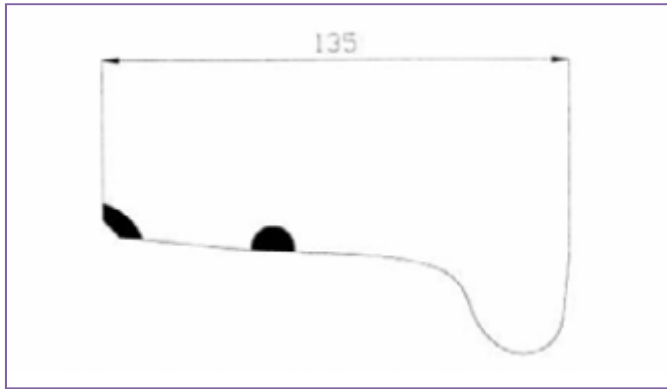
Posición Típica de Inicio de Grieta Térmica.
